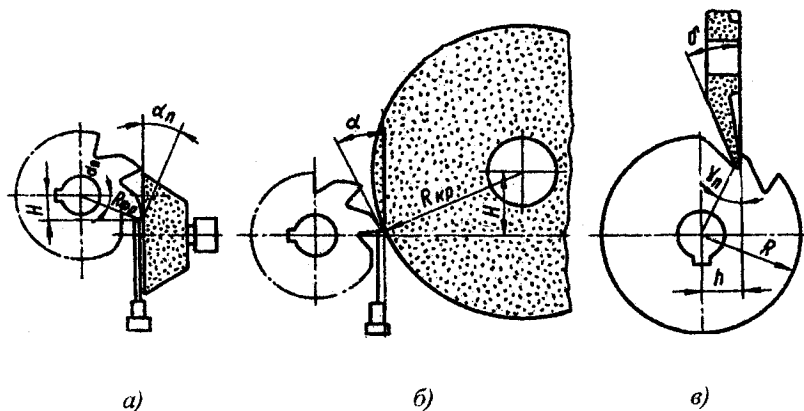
Схеми заточування циліндричних фрез з прямими канавками
